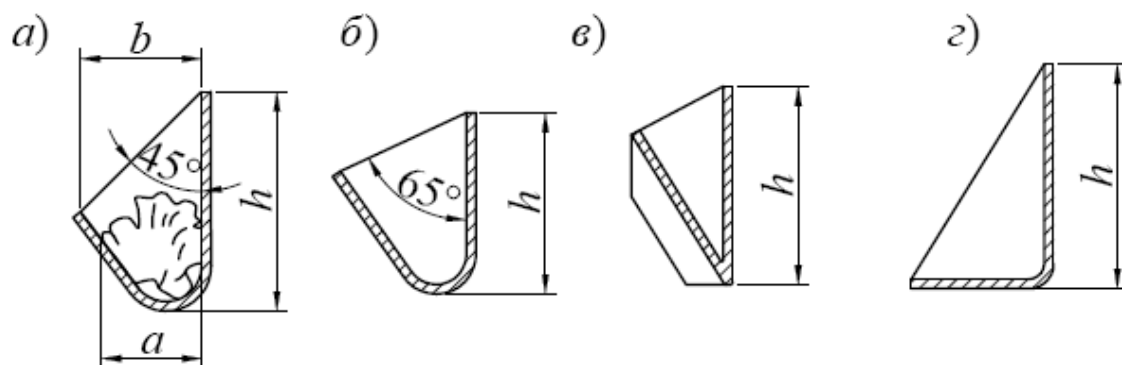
Типы элеваторных ковшей: *а* – полукруглый мелкий (типа М); *б* – полукруглый глубокий (типа Г); *в* – остроугольный с бортовыми направляющими (типа О); *г* – чешуйчатый
